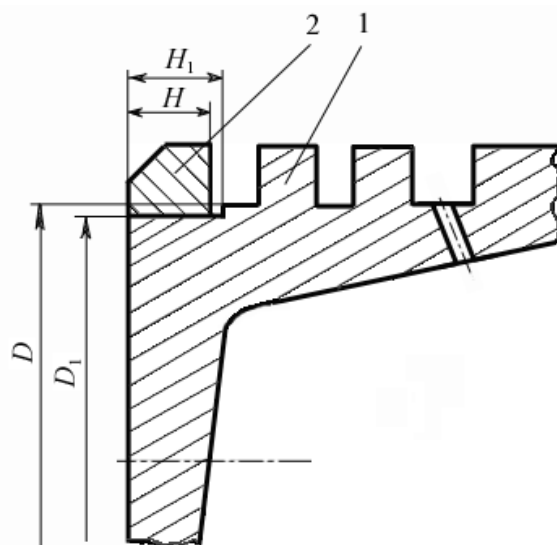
Схема установки дополнительной ремонтной детали (ДРД) при восстановлении канавки под поршневое кольцо:
